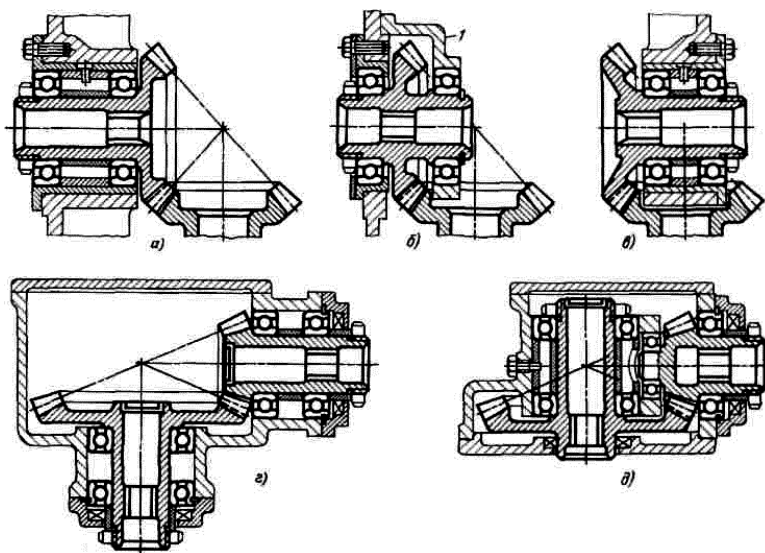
Уменьшение габаритных размеров конической передачи
